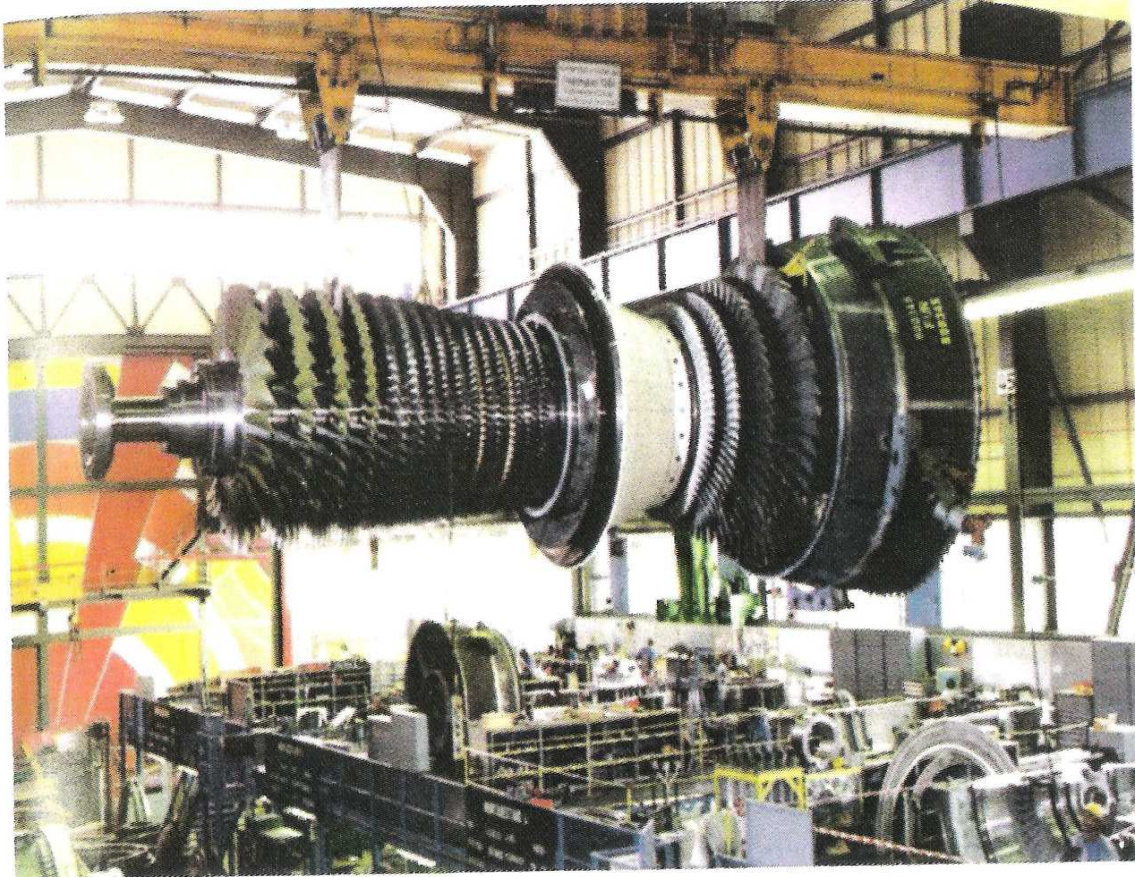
Rotor turbina de gas SGT6 4000F (cortesía de Siemens-Westinghouse).
